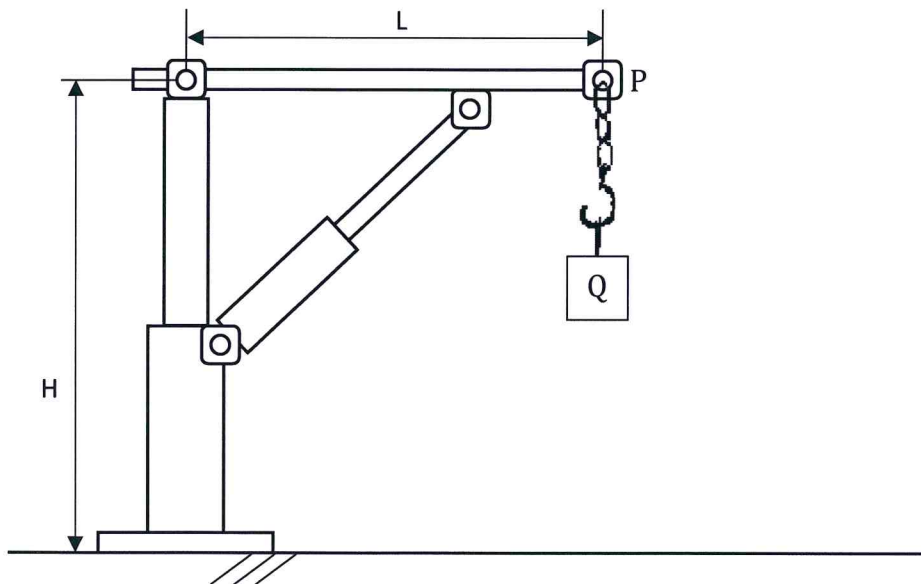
Schema del sollevatore nella sua posizione di massima altezza.
